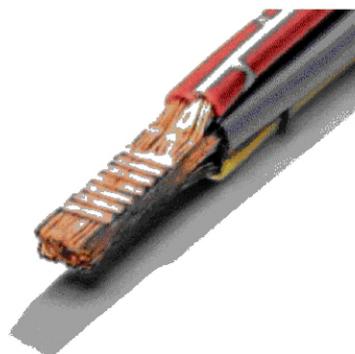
Одностороннее сваривание ультразвуковой сваркой
